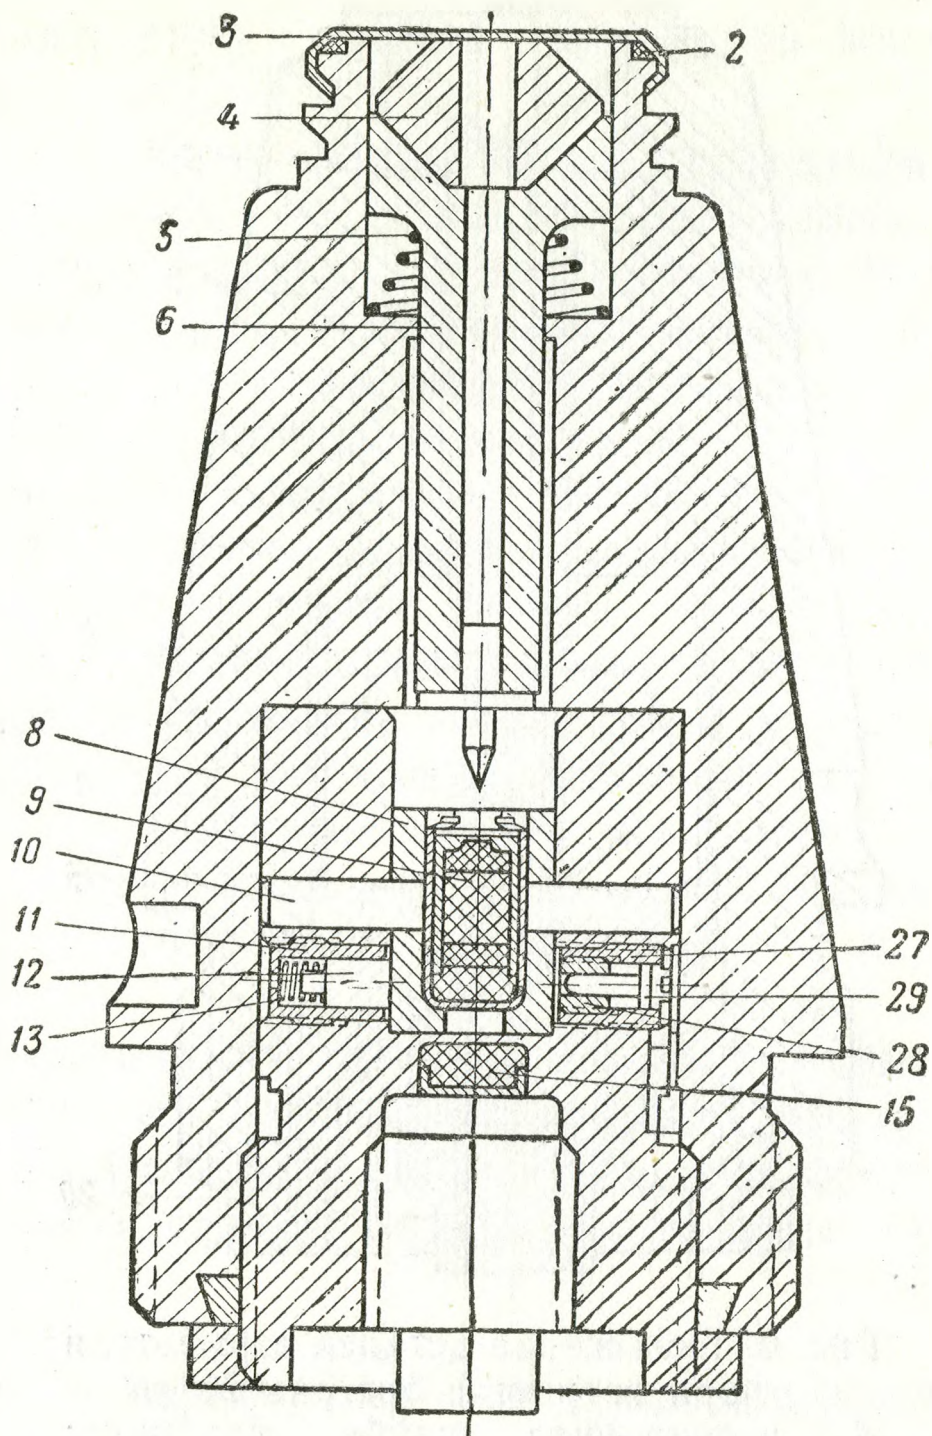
Положение взрывателя на полете: 2—прокладка под мембрану; 3—мембрана; 4—реакционная шайба ударника; 5—пружина ударника; 6—ударник с жалом; 8—поворотный движок; 9—капсюль-детонатор; 10—ось; 11—втулка центробежного стопора; 12—центробежный стопор; 13—пружина центробежного стопора; 15—передаточный заряд; 27—втулка порохового предохранителя; 28—гайка; 29—стопор
